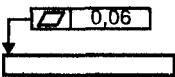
Правила простановки допусков формы и расположения
